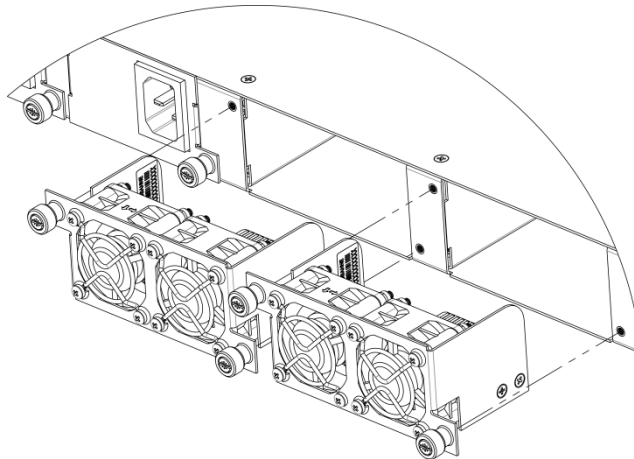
Блок вентиляции в SBC-3000 на базе SMG-3016. Крепление в корпус
